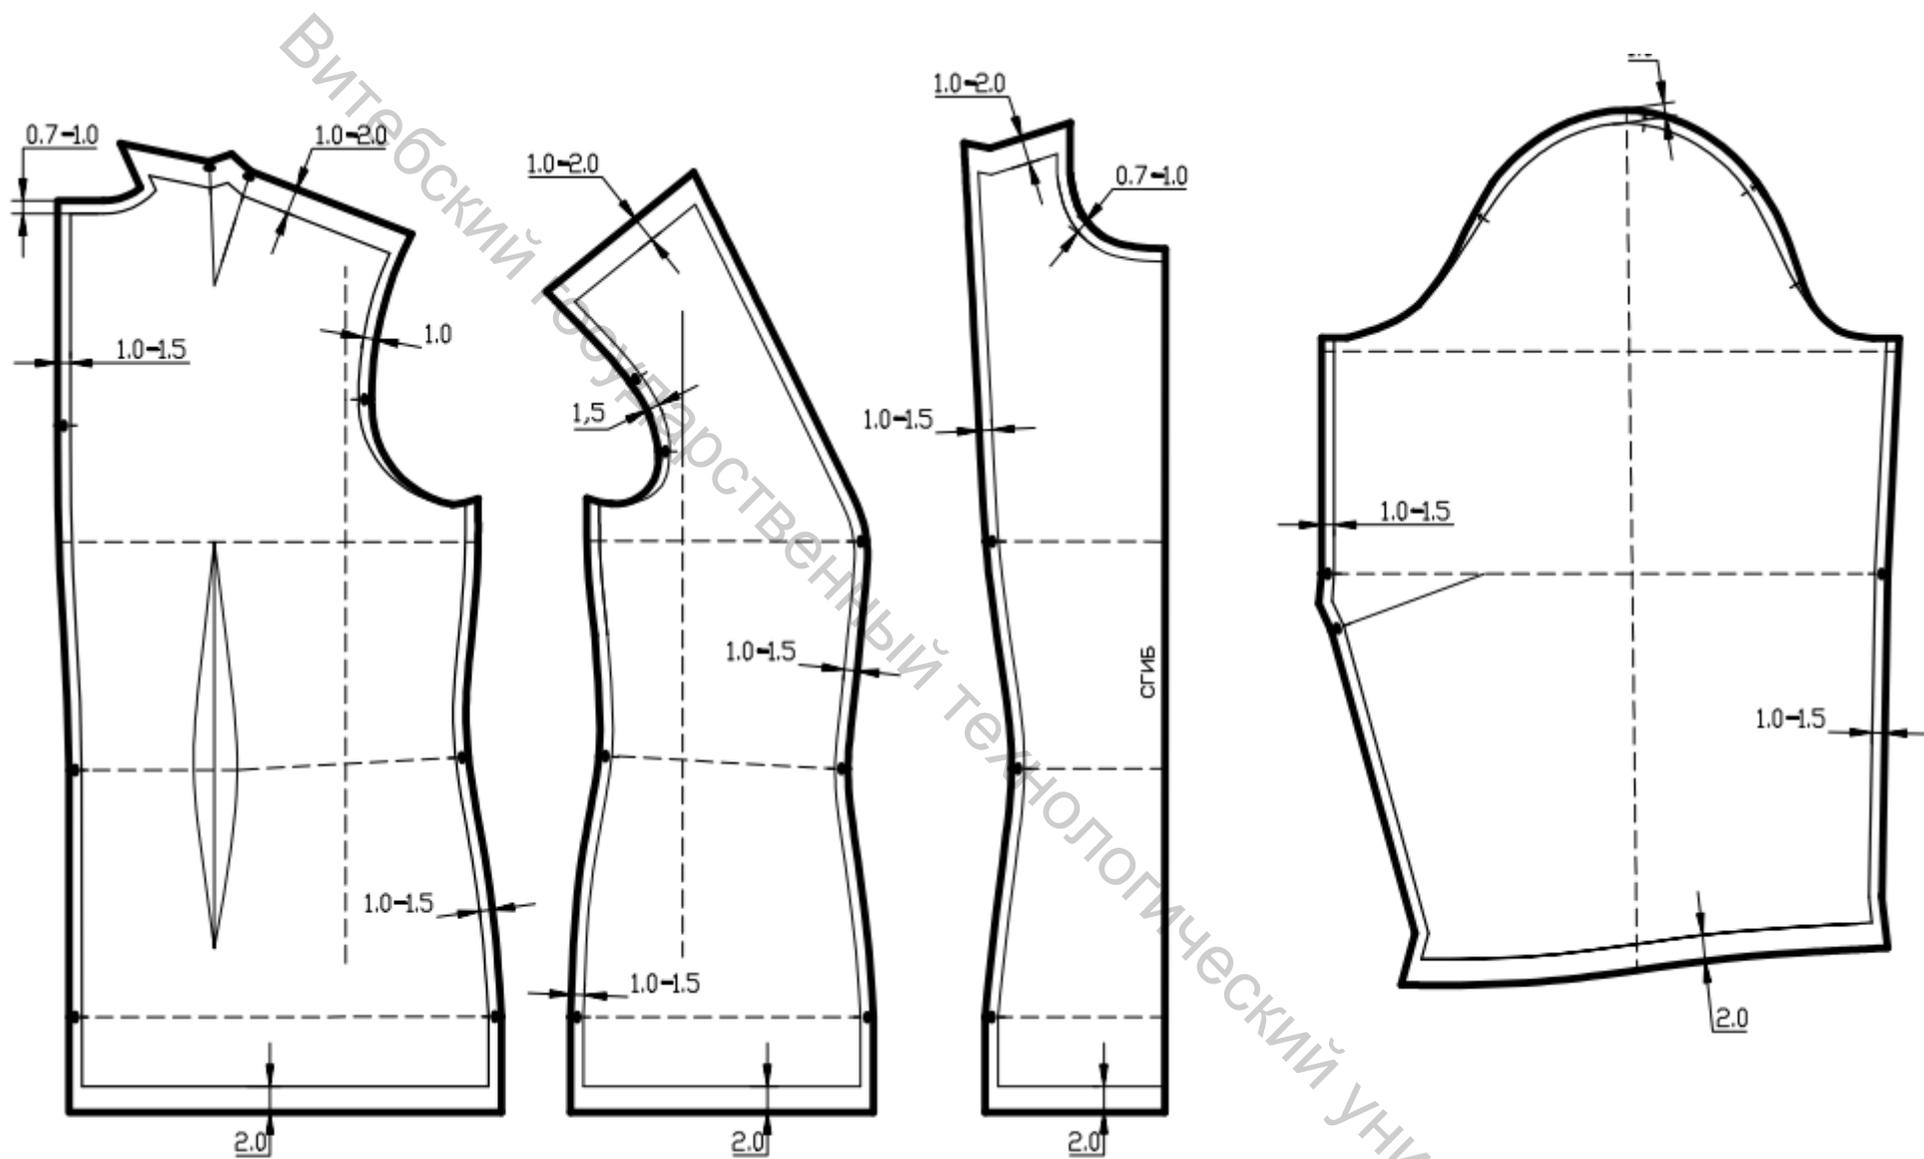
Схема размещения припусков на уточнение конструкции деталей платья и сметочных линий
